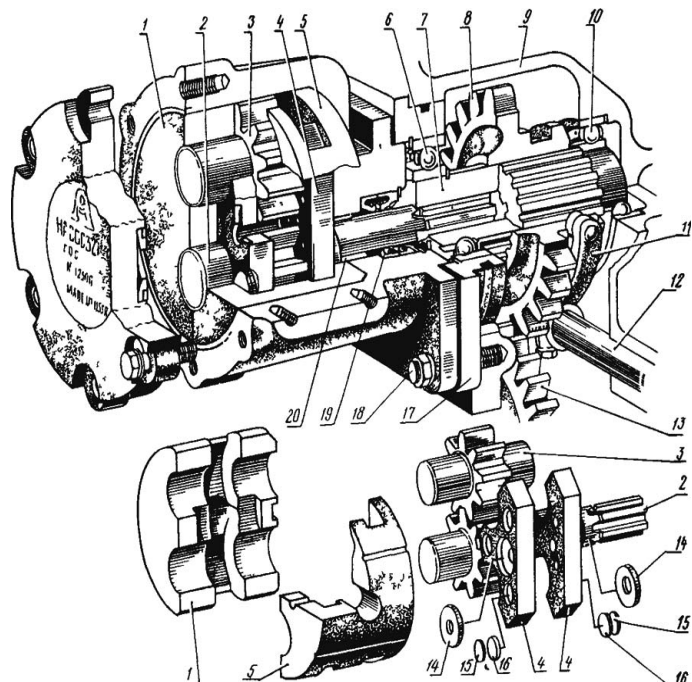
Масляный насос. 1 — подшипниковая обойма; 2 — ведущая шестерня; 3 — ведомая шестерня; 4 — пластик; 5 — поджимная обойма; 6, 10 — шарикоподшипники; 7 — вал привода; 8 — шестерня; 9 — корпус гидроагрегатов; 11 — вилка; 12 — валик управления; 13 — промежуточная шестерня; 14 — манжета; 15 — шайба; 16 — манжета; 17 — стакан подшипника; 18 — шпилька; 19 — манжета; 20 — втулка центрирующая
